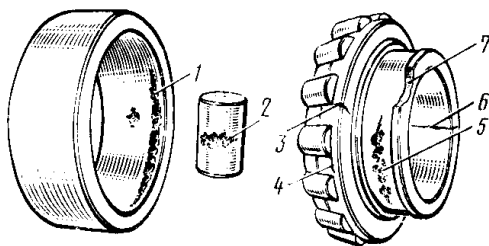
Дефекты деталей роликового подшипника: 1 – раковины на дорожке качения наружного кольца; 2 – раковины на цилиндрическом ролике; 3 – излом сепаратора; 4 – трещина у основания перемычки; 5 – раковины на внутреннем кольце; 6 – трещина кольца; 7 – откол борта
